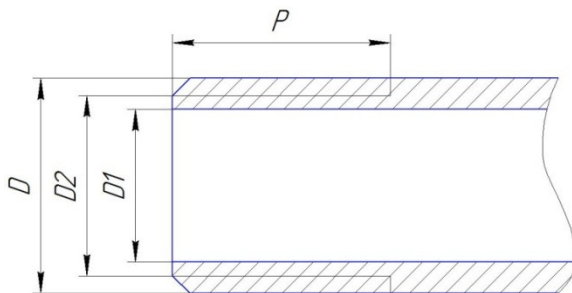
Присоединительные размеры штуцера рубашки обогрева
